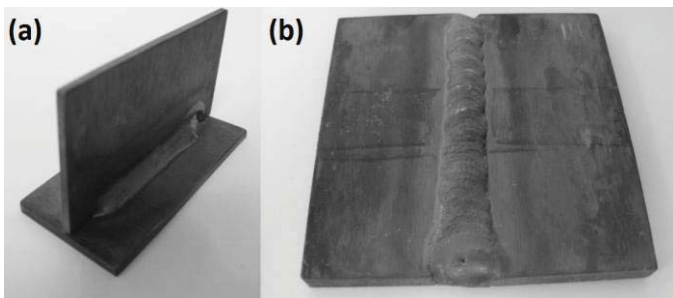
Soldadura de acero (a) y soldadura de una aleación de titanio (b) usando ESC [9], [10]
